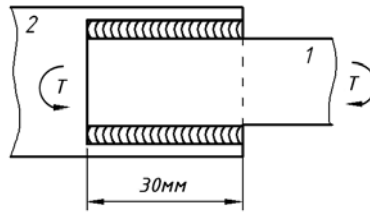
Сварное соединение полосы с косынкой
